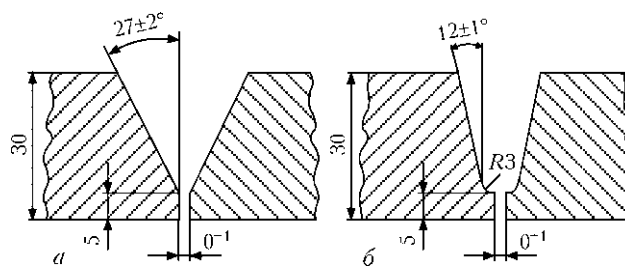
Схема кромок для лазерной сварки V- (а) и U-образной (б) разделки
